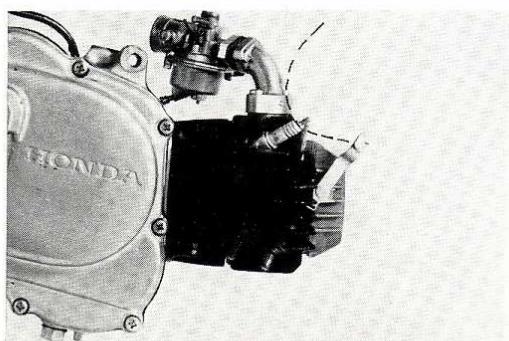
DEMONTAGE DU CABLE LEVE-SOUPAPE.
